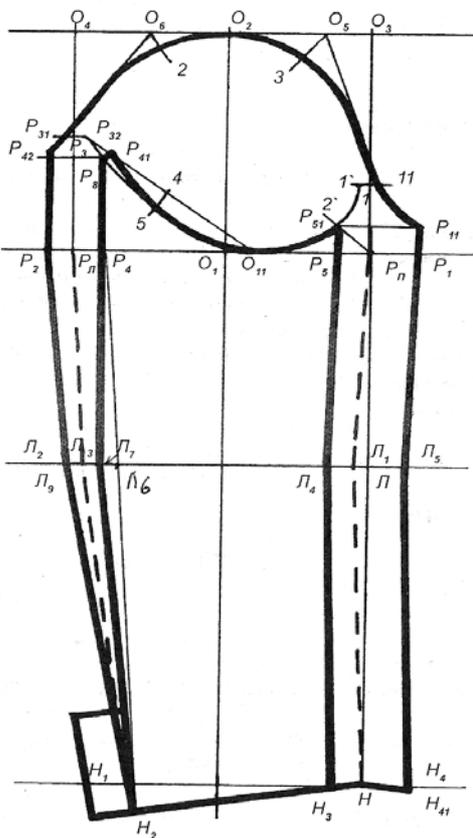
Чертеж конструкции двухшовного рукава пальто
